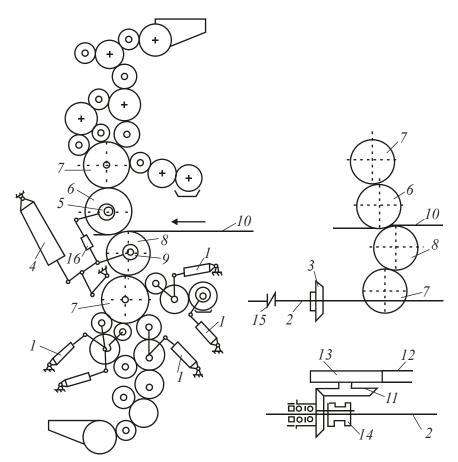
Секция двусторонней офсетной печати: 1, 4 – гидроцилиндры; 2 – вал; 3, 11–13 – зубчатые колеса; 5, 9 – эксцентричные втулки; 6, 8 – офсетные цилиндры; 7 – формный цилиндр; 10 – бумажная лента; 14, 15 – муфты; 16 – гайка с левой и правой резьбой
